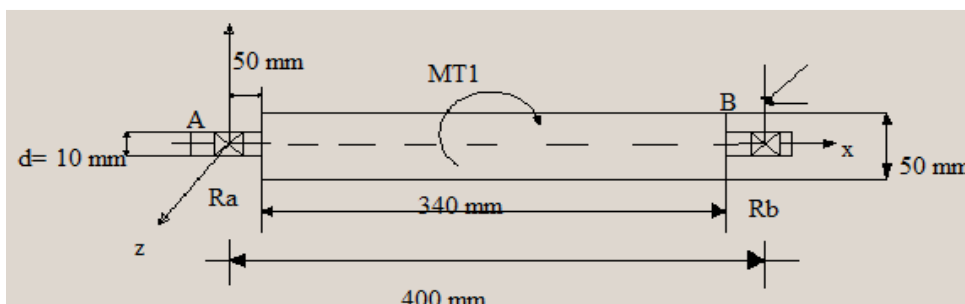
FUERZAS QUE ACTÚEN EN EL RODILLO
